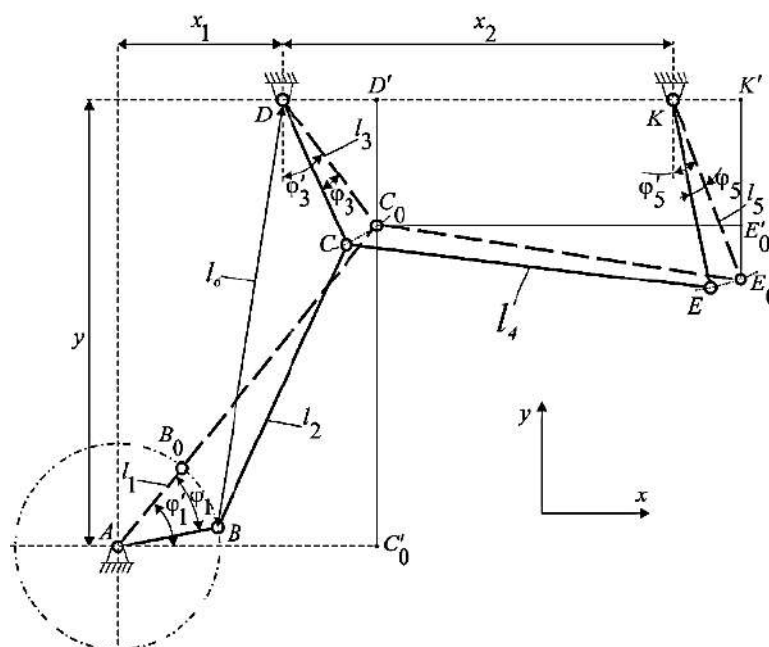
Расчетная схема сортировочного устройства с шарнирно-шестизвенным механизмом с коромыслами разной длины
